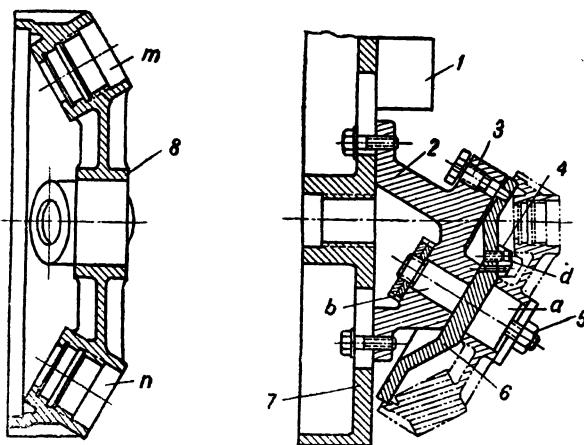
Поворотное приспособление для обработки изделия с системой отверстий.
